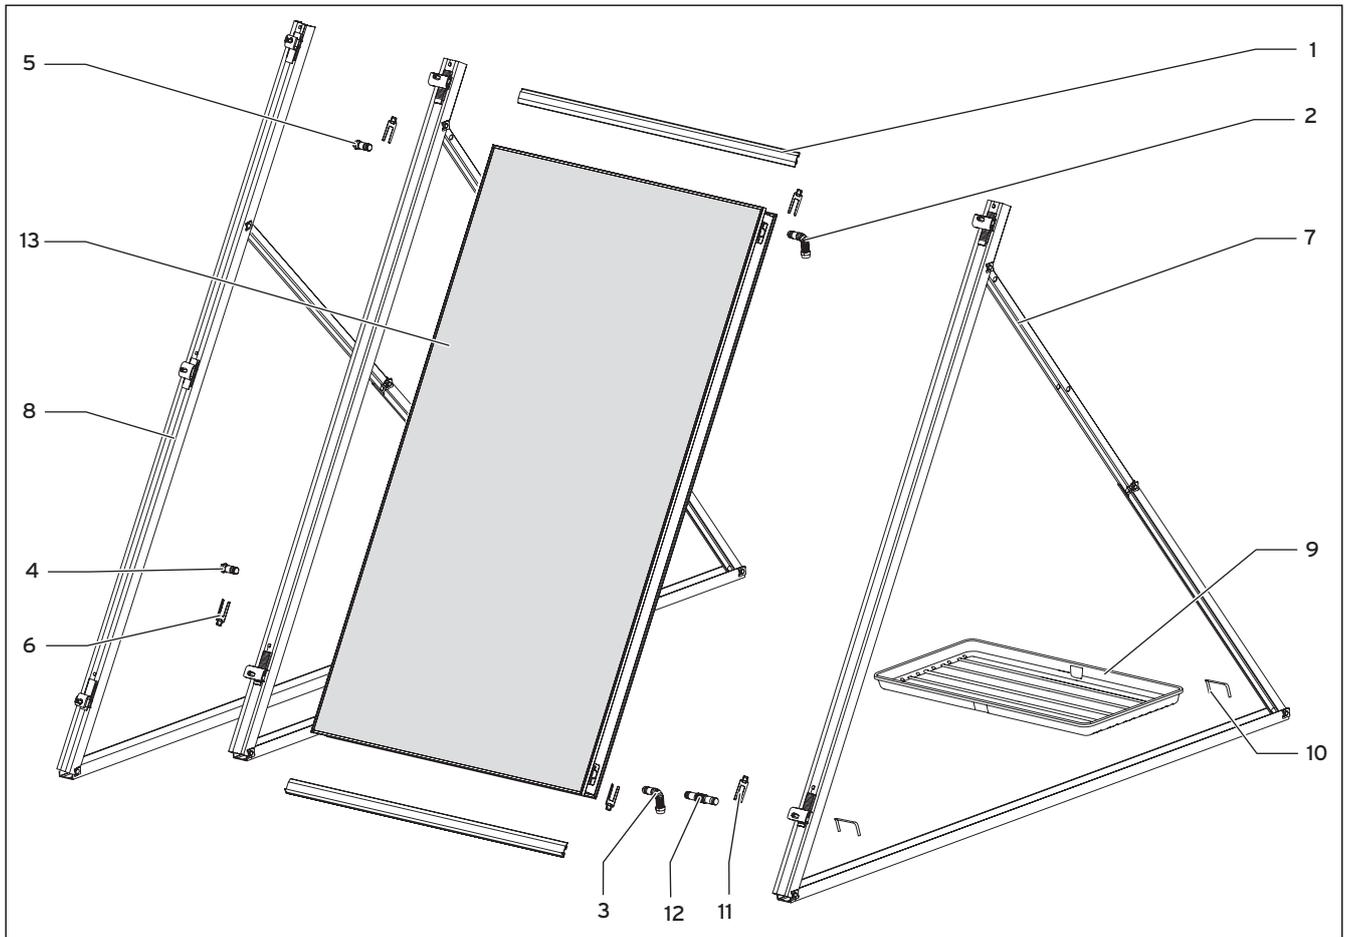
Kit de montage sur toit plat (ici : capteur vertical)
